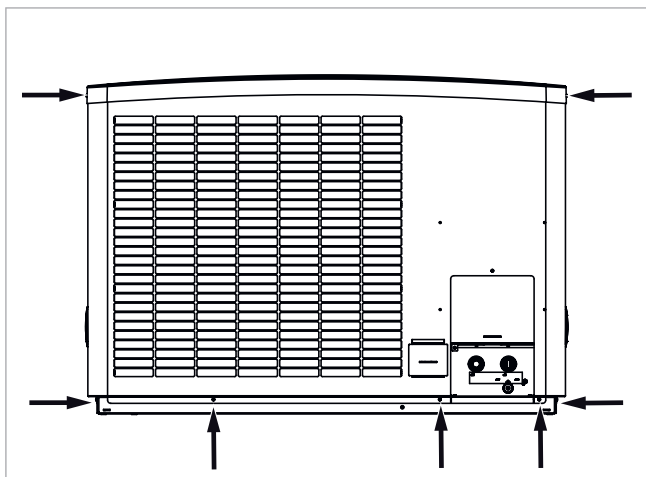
Hinteres Gehäuse-Element von SolvisLea 8,3 Premium abschrauben und entfernen
